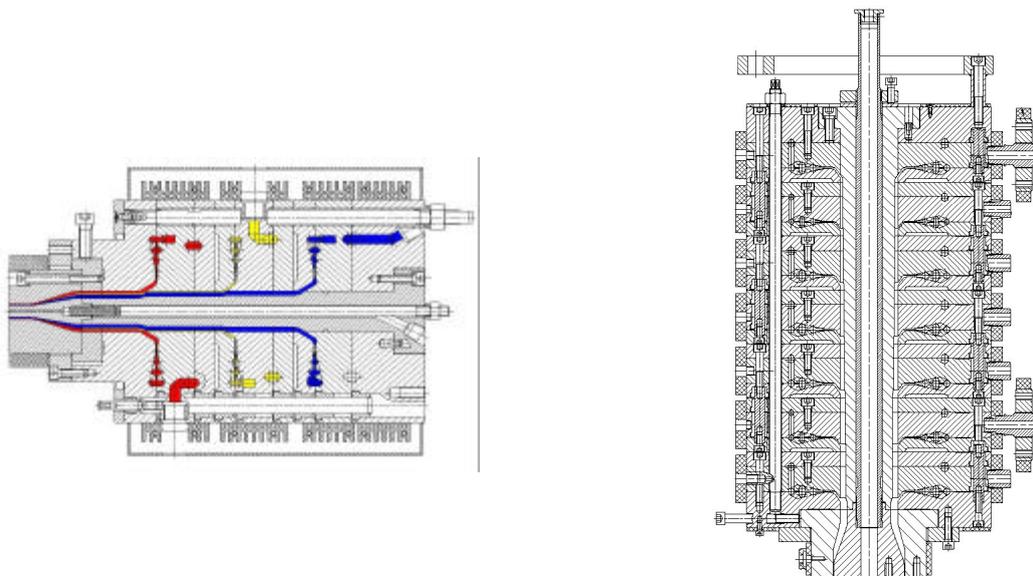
Circularverteiltertechnik – Kühlbares Werkzeug für Kleinrohre und Siebenschichtkopf
